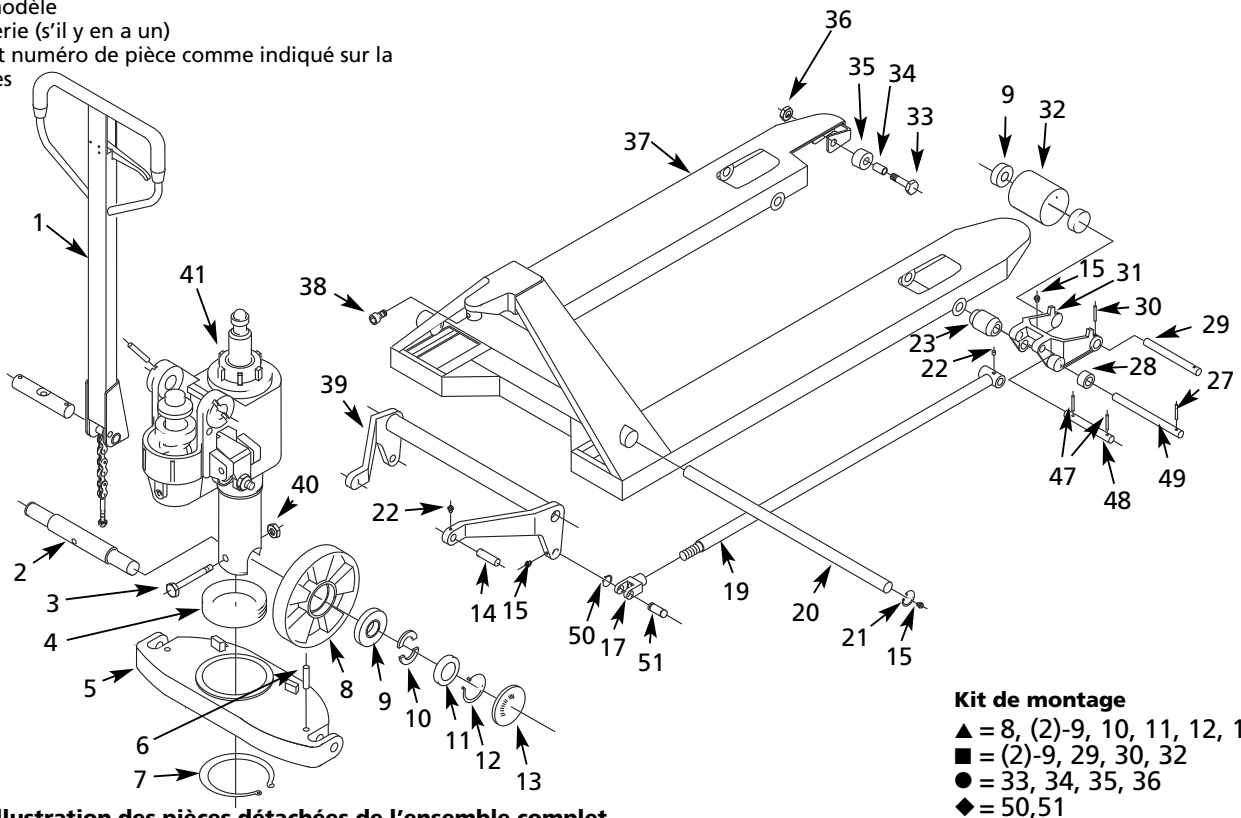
Illustration des pièces détachées de l'ensemble complet
